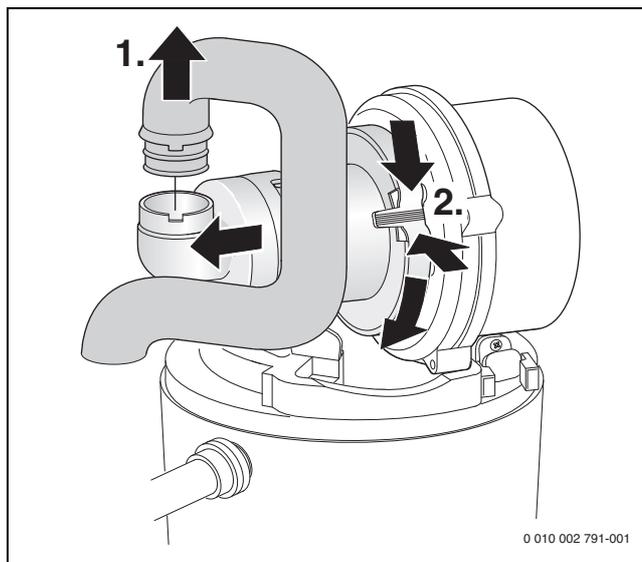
Démontez le tube d'aspiration et le mélangeur
